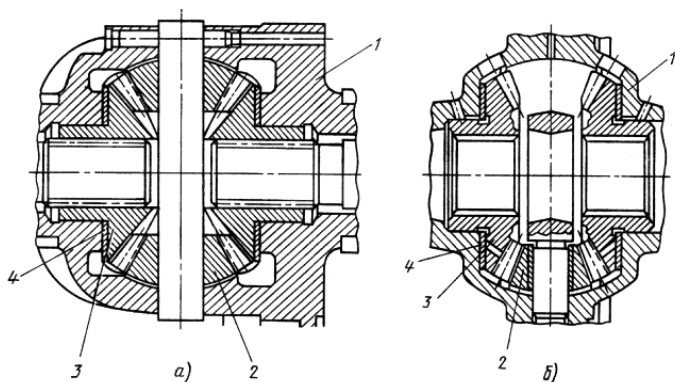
Конструкция межколесного симметричного шестеренчатого дифференциала: *а* — с двумя сателлитами; *б* — с четырьмя сателлитами
